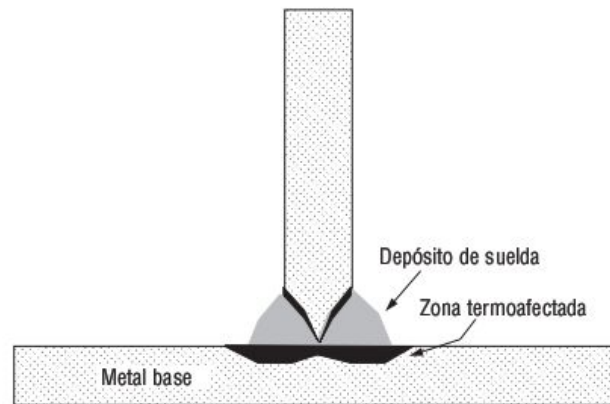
Zona termoaffectada producida durante la soldadura.
